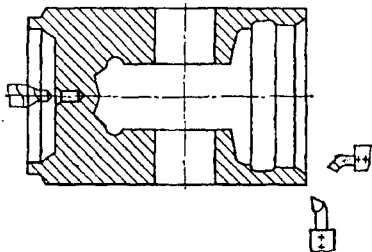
Схема обробки бази в поршні уніфікованого поршневого компресора УУ-220.
